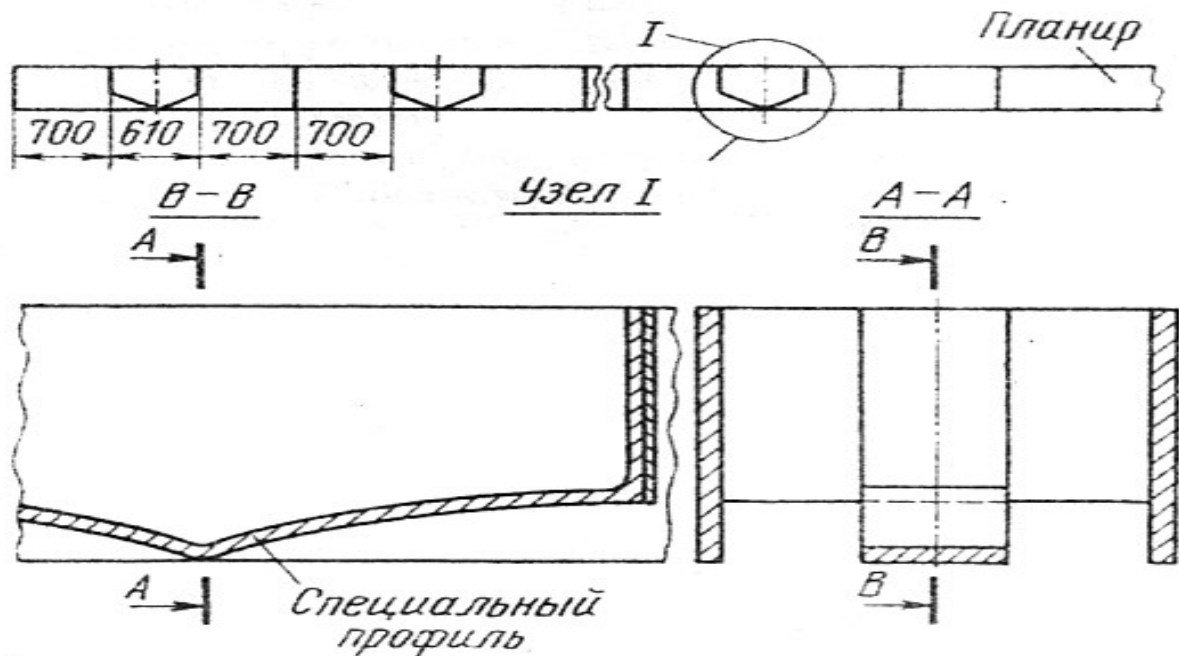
Конструкція планірної штанги з пристроєм для пресування вугілля
